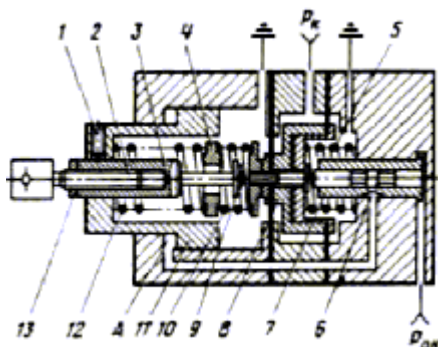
Схема гидроусилителя регулятора: 1 – винт; 2 – серьга; 3 – шток; 4 – тарелка; 5 – уравновешивающая пружина; 6 – золотник; 7 – втулка; 8 – мембранный блок; 9 – прокладка; 10, 12 – пружины; 11 – поршень; 13 – гайка; А – полость
